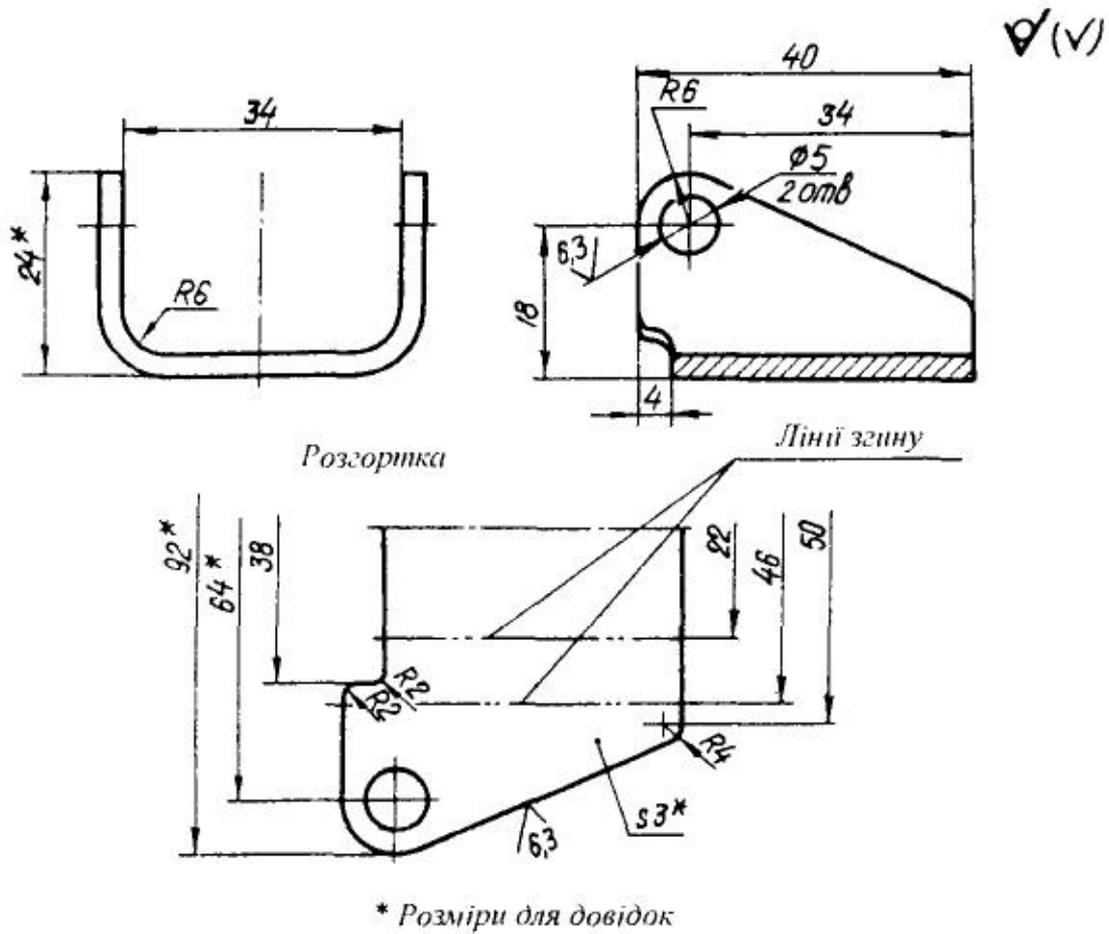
Креслення штампованої деталі з розгорткою її поверхні.
